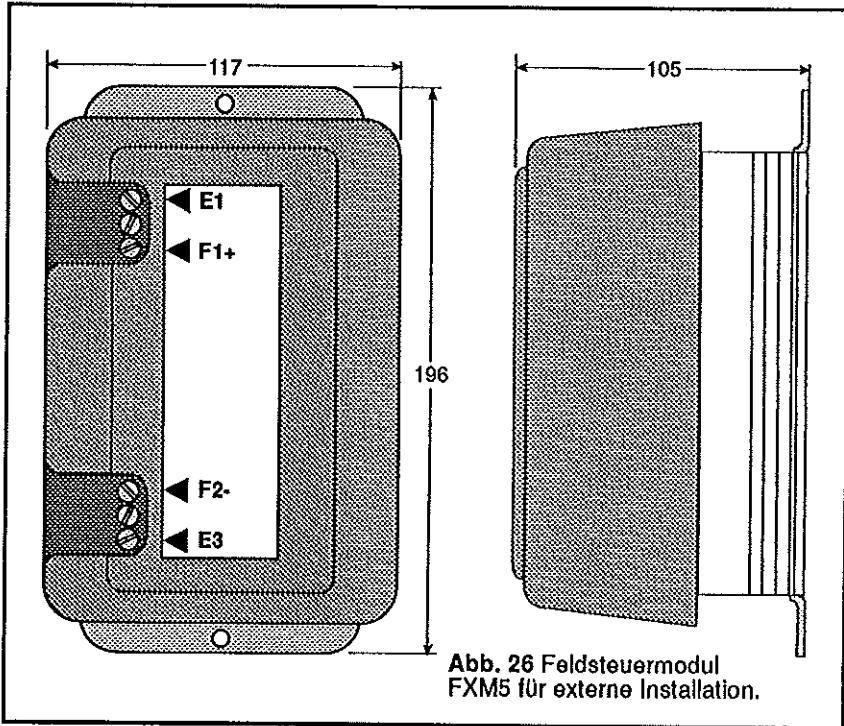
Feldsteuermodul FXM5 für externe Installation.
